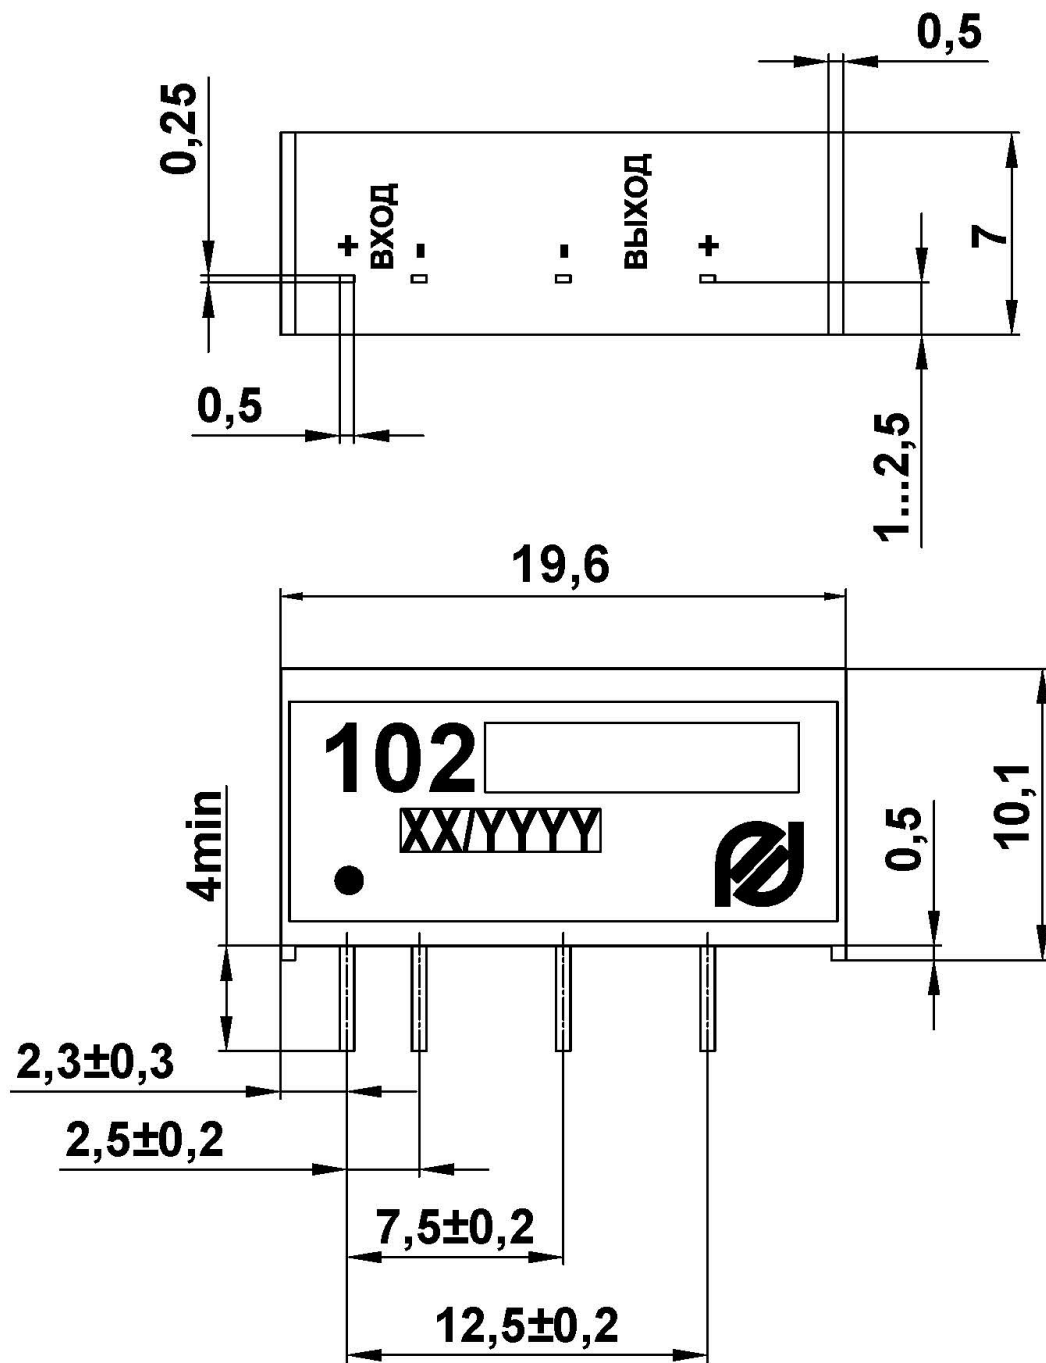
Габаритный чертеж одно- (двух) ваттных одноканальных модулей в конструктиве «Н», корпусного исполнения
